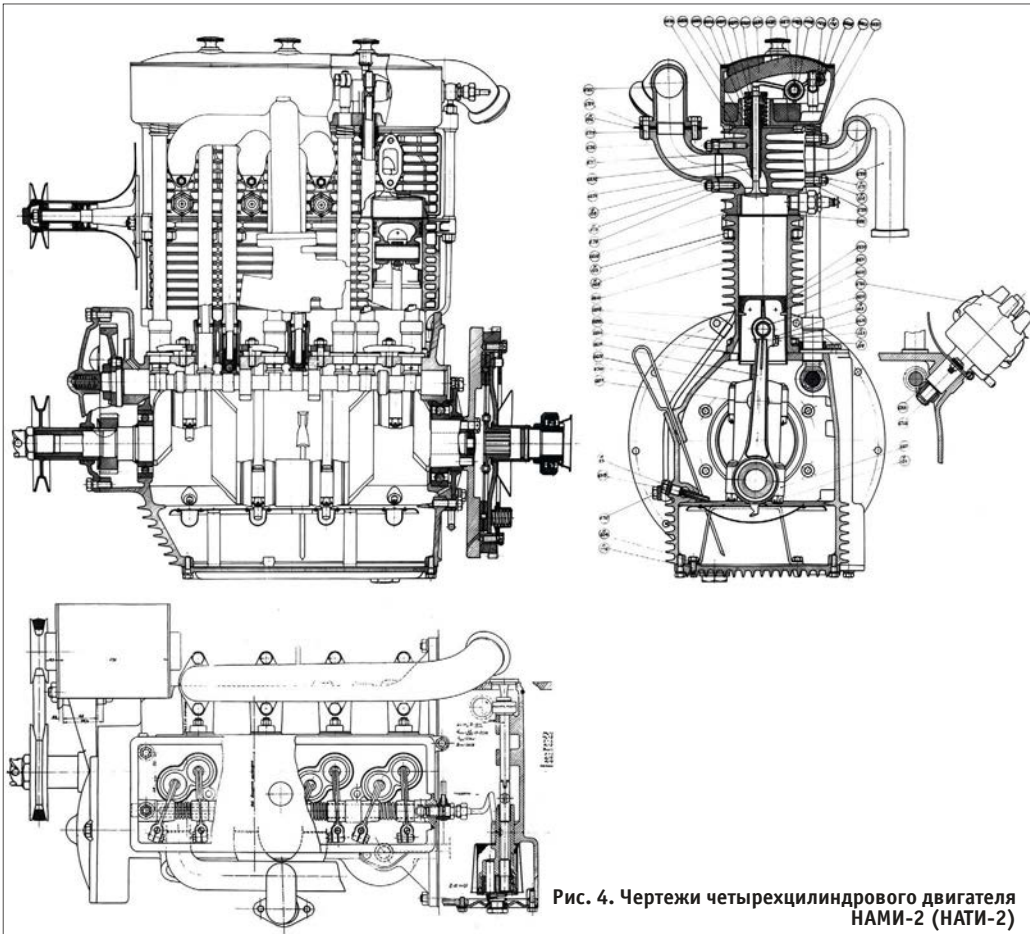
Чертежи четырехцилиндрового двигателя НАМИ-2 (НАТИ-2)
